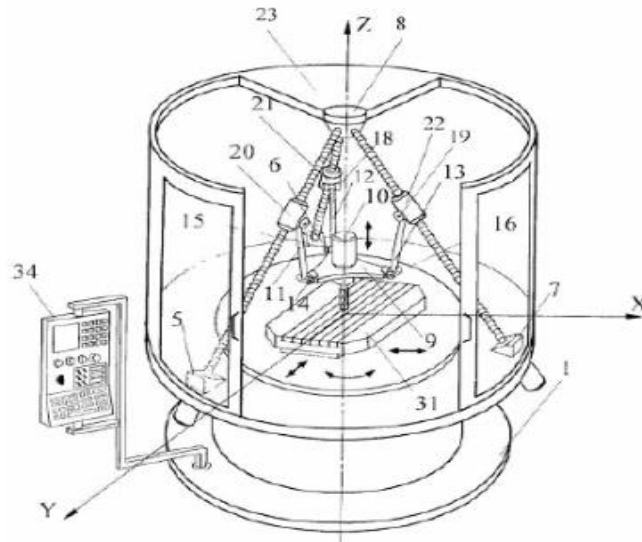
Багатокоординатний свердлильно-фрезерний верстат
